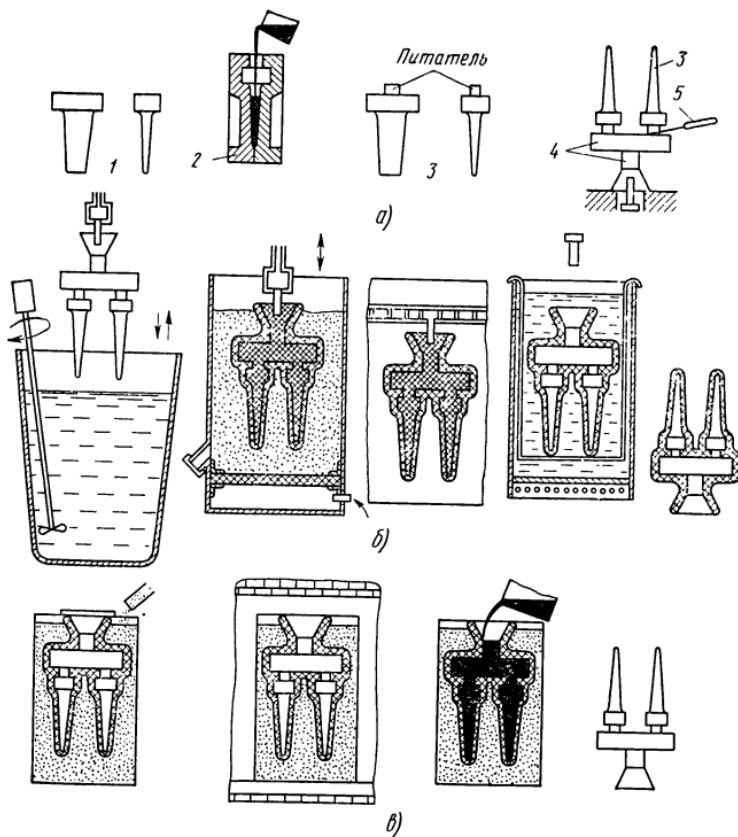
Схема процесса изготовления отливок по выплавляемым моделям:
